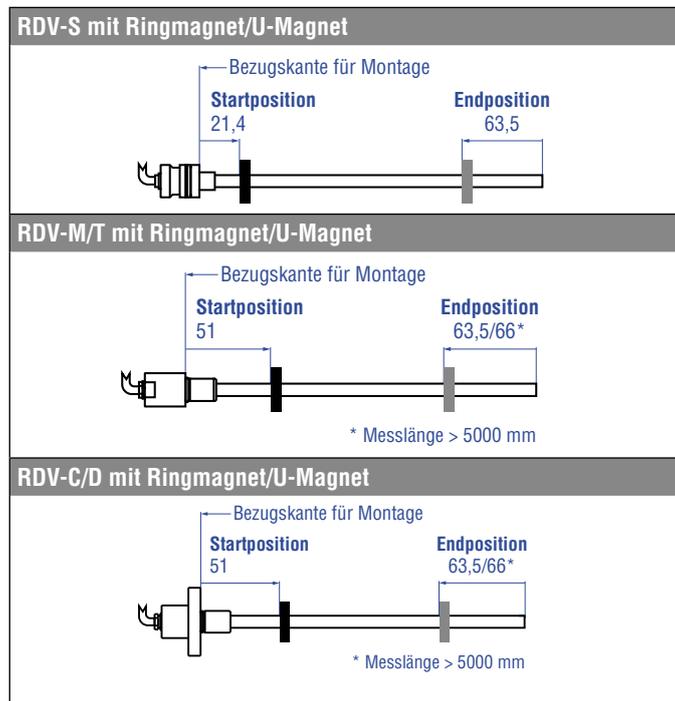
Start- und Endpositionen der Magnete für RDV mit Ring- und U-Magneten
